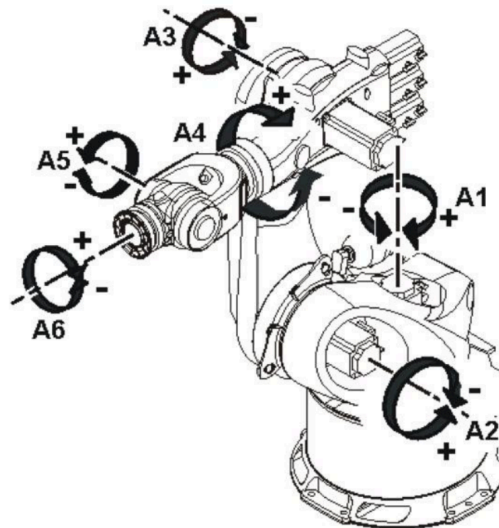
ejes de giro del robot KR 600 R2830 del fabricante KUKA. Fuente: KUKA.
